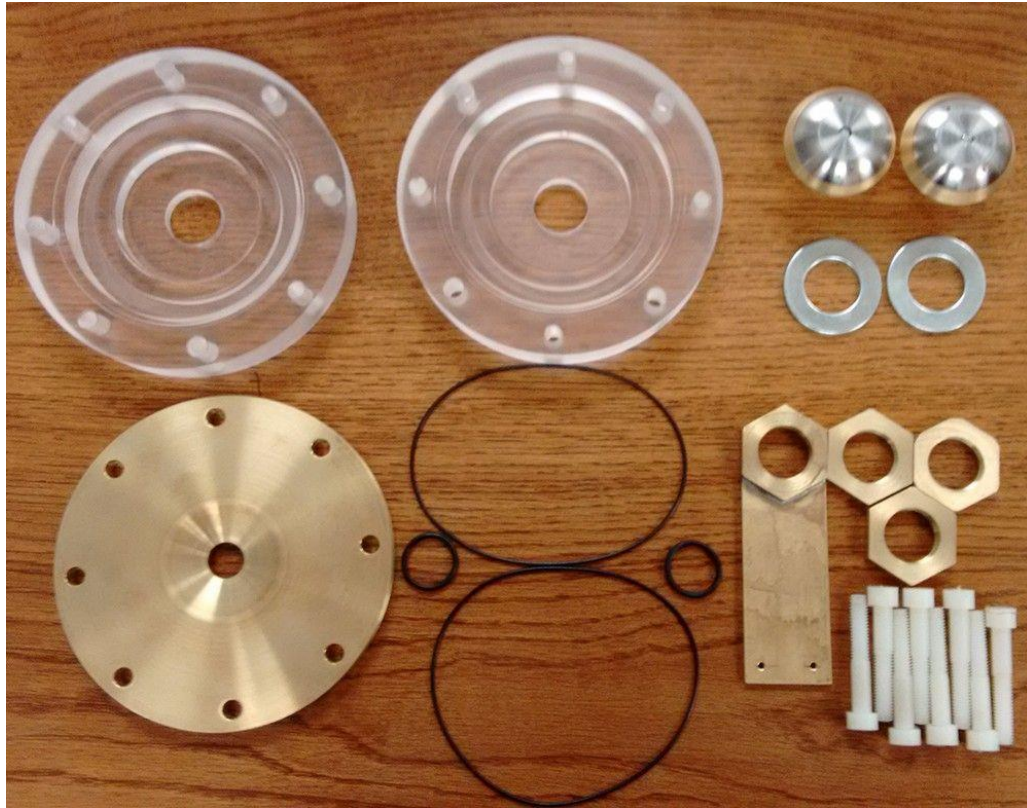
Conjunto completo de componentes del nuevo interruptor de chispa.
